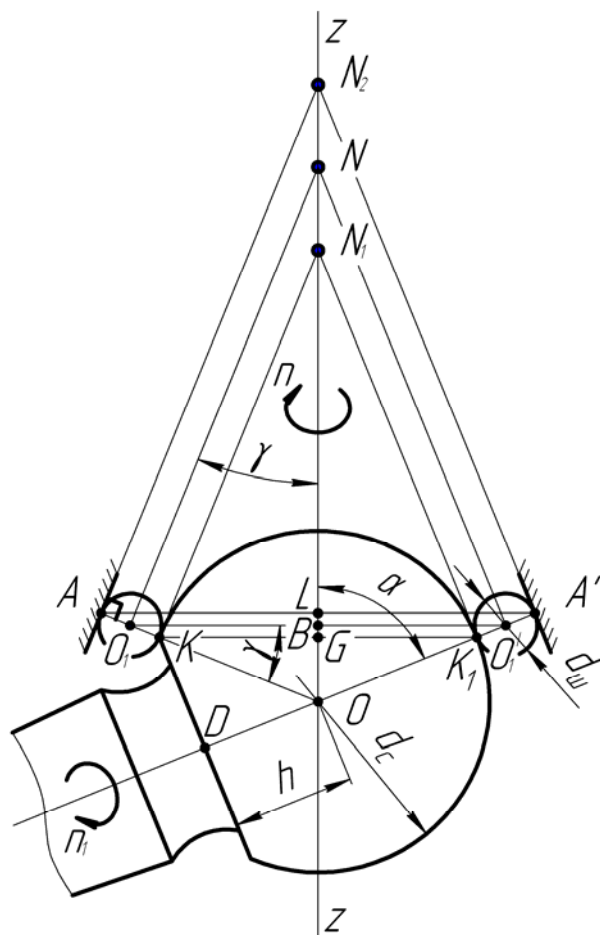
Кинематическая схема процесса обкатки неполной сферической головки шарового пальца
